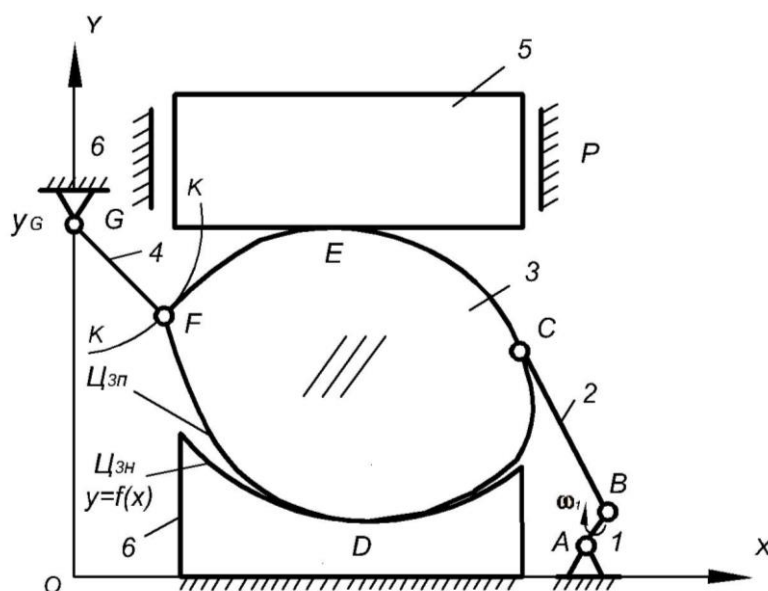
Центроидный механизм с перекатывающимся рычагом
